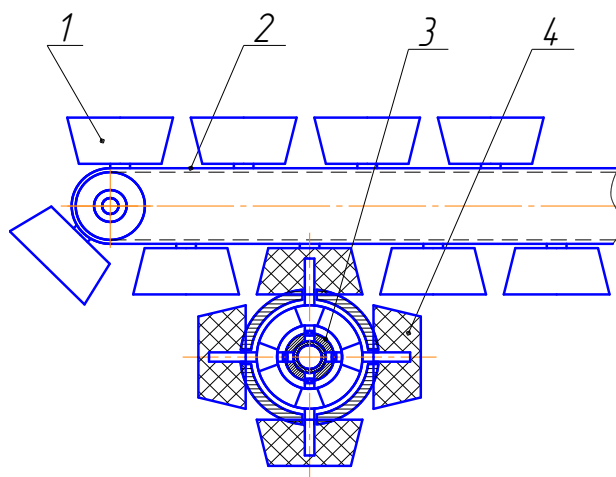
Устройство для очистки и мойки кормушек 1 – Кормушка; 2 – транспортер ленточный; 3 – механизм очищающий; 4 – щетка;
